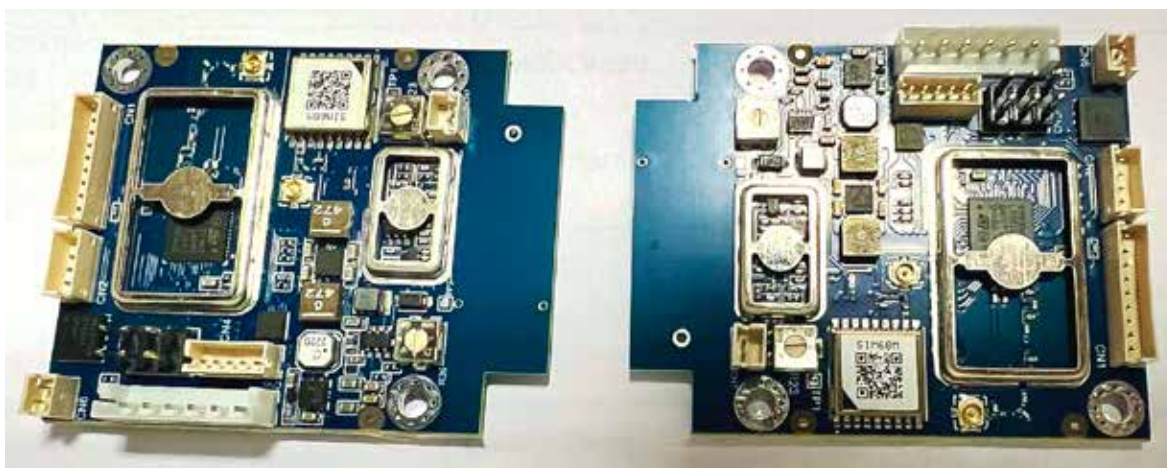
Внешний вид исполнения платы контроллера
